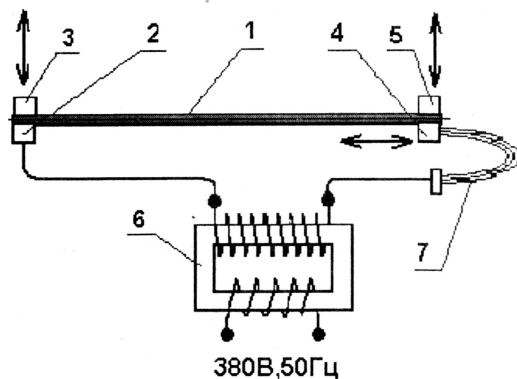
Схема электроконтактного нагрева прутка: 1 — заготовка; 2 — неподвижный контакт; 3 — прижимной неподвижный контакт; 4 — подвижный контакт; 5 — подвижный прижимной контакт; 6 — силовой трансформатор; 7 — гибкая шина
